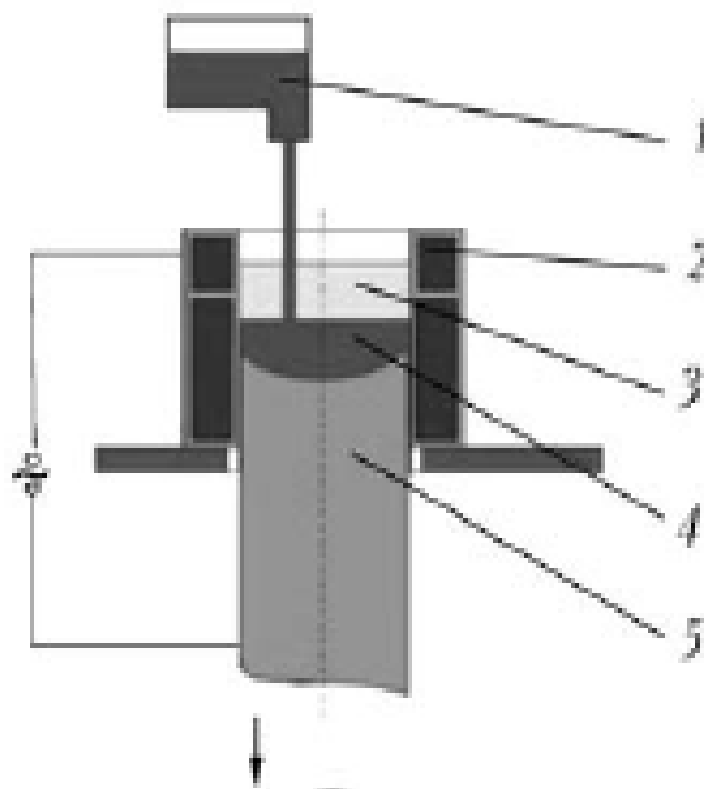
Схема процесу ЕШП РМ [10]: 1 – заливочний пристрій для подачі рідкого металу в кристалізатор; 2 – струмопідвідний кристалізатор; 3 – шлакова ванна; 4 – металева ванна; 5 – злиток
